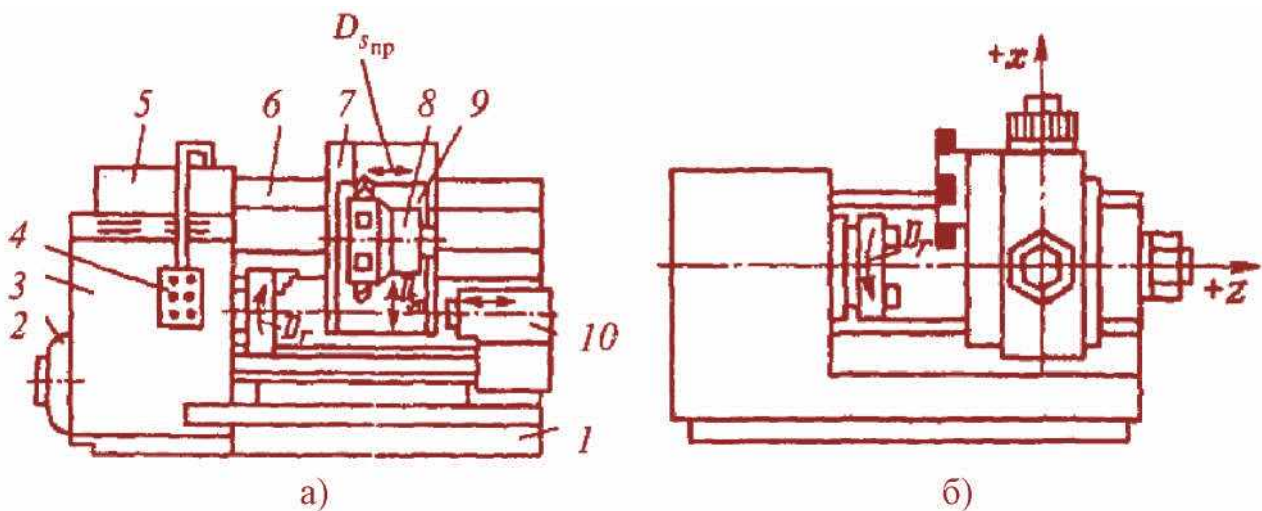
Загальні види токарних верстатів з ЧПК
